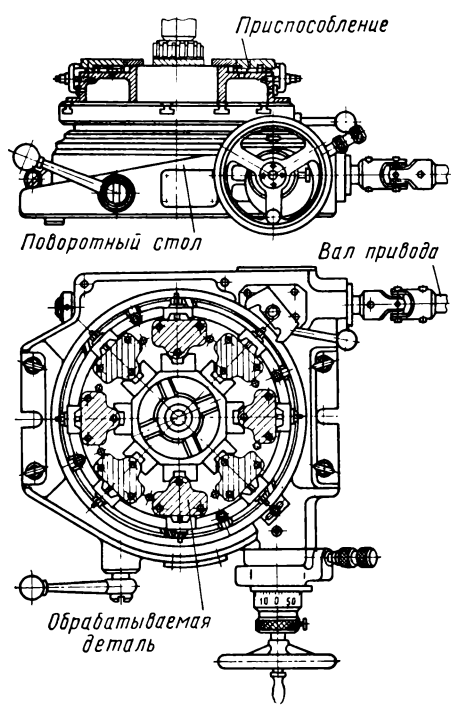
Пример наладки поворотного круглого стола для непрерывного фрезерования
